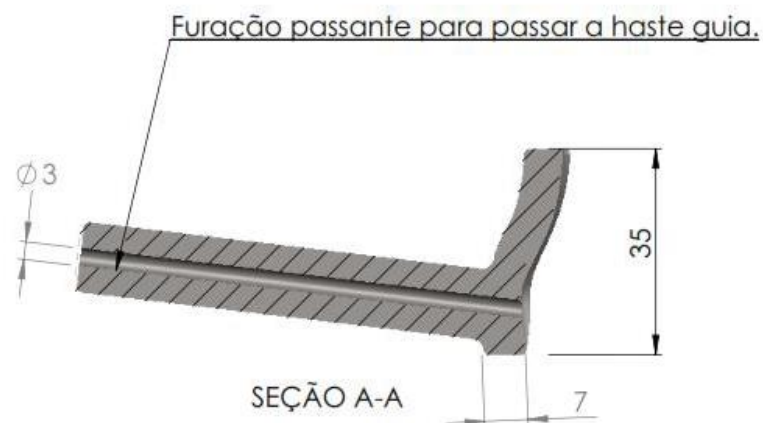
Vista da furação passante do Guia DCS 95 mini-open
